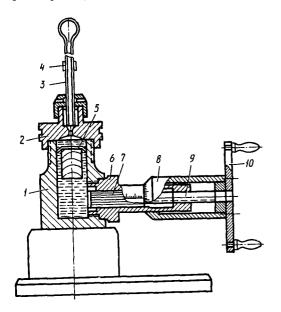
Объемомер: I — корпус, 2 — крышка, 3 — трубка, 4 — указатель, 5 — скоба, 6 — горизонтальный цилиндр, 7 — поршень. 8 — обойма, 9 — микрометрический винт, 10 — рукоятка
